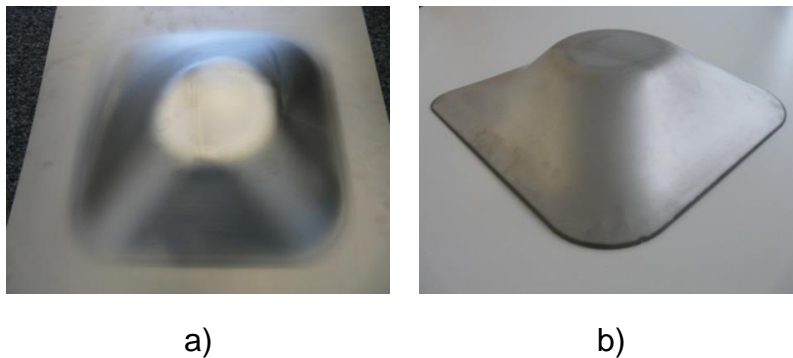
Cara exterior de pieza descontaminada: a) antes y b) después de ser recortada.
